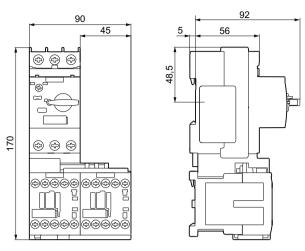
Arrancador inversor S00, AC/DC, bornes de tornillo 3RA2210-..A
